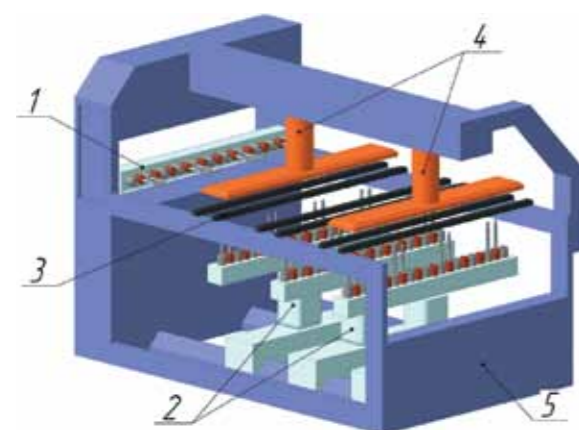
Сверлильно-присадочный станок с различными многошпиндельными головками (упрощенная схема).
